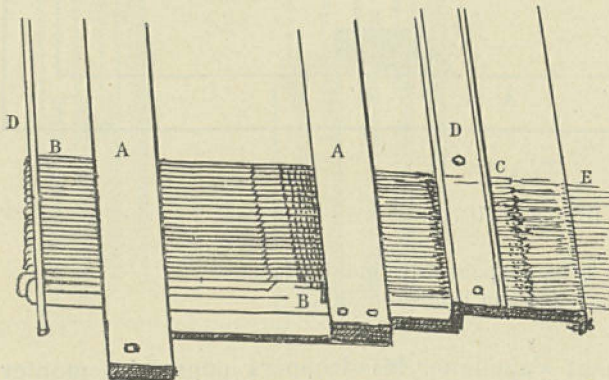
VUE PRISE AU-DESSUS DU JACQUARD.
